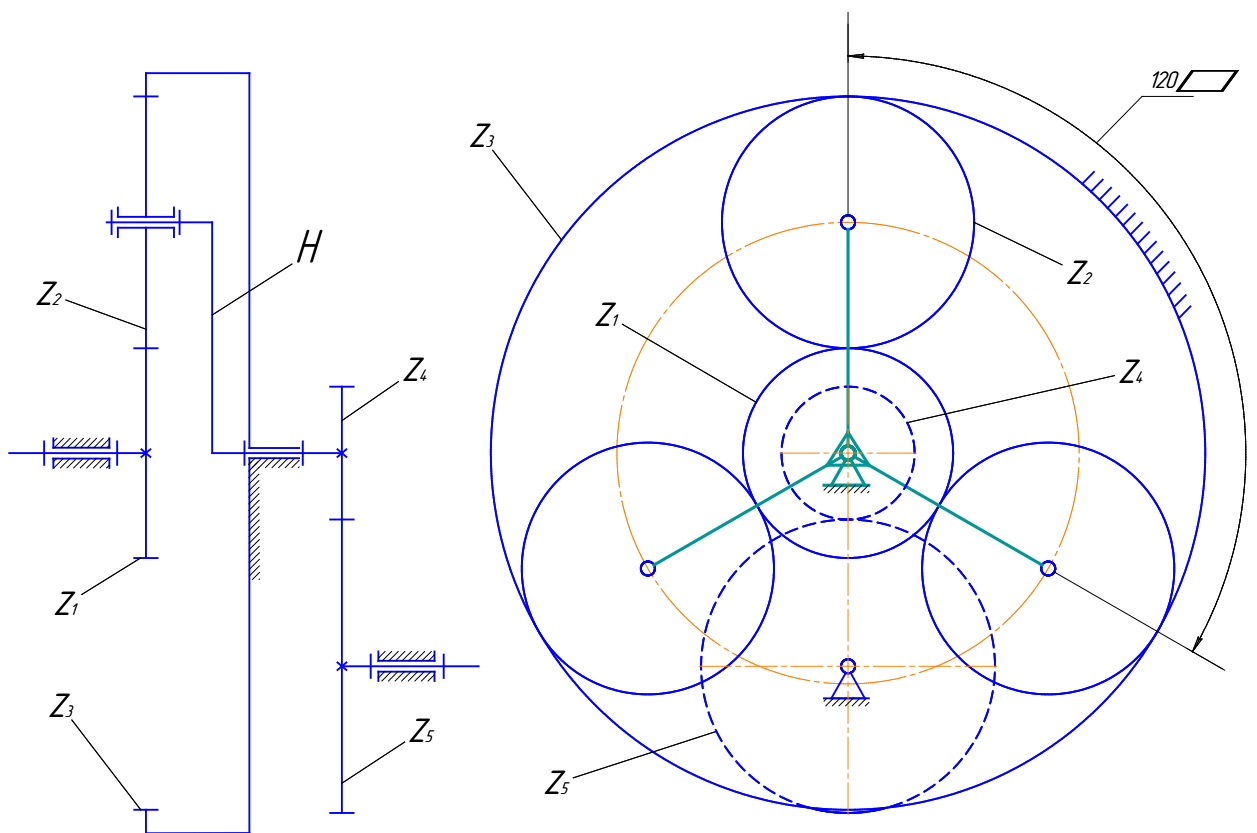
Кинематическая схема сложного зубчатого механизма
